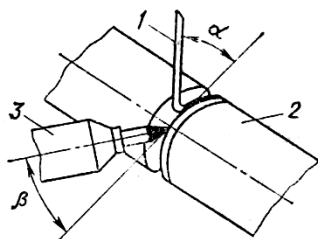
Схема сварки нагретым газом (прутковая сварка):
